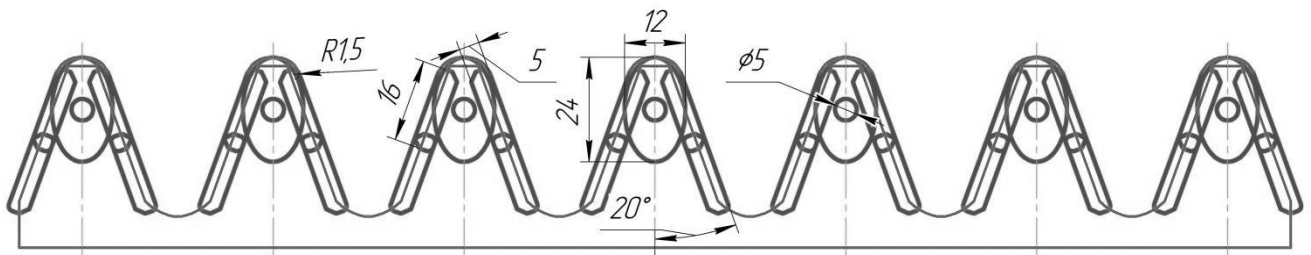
Групповое расположение сменных режущих твердосплавных пластин в исходном контуре инструментальной рейке
